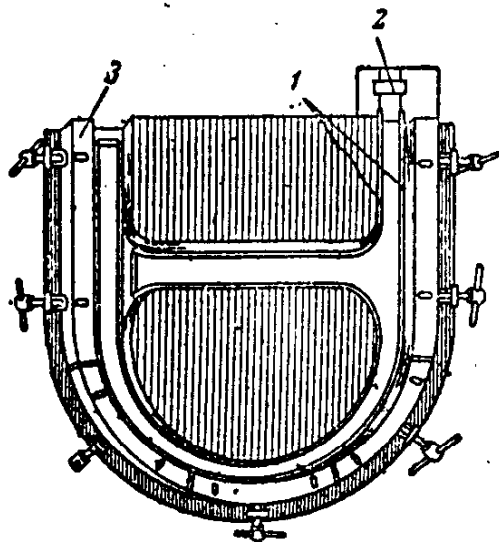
Стационарный сплошной закрытый нагреватель-шаблон для выклейки обшивок из шпона.
